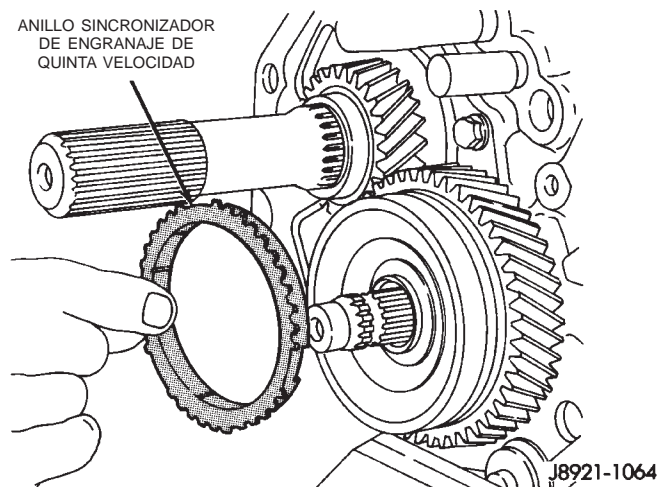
Desmontaje de anillo sincronizador de engranaje de quinta velocidad
